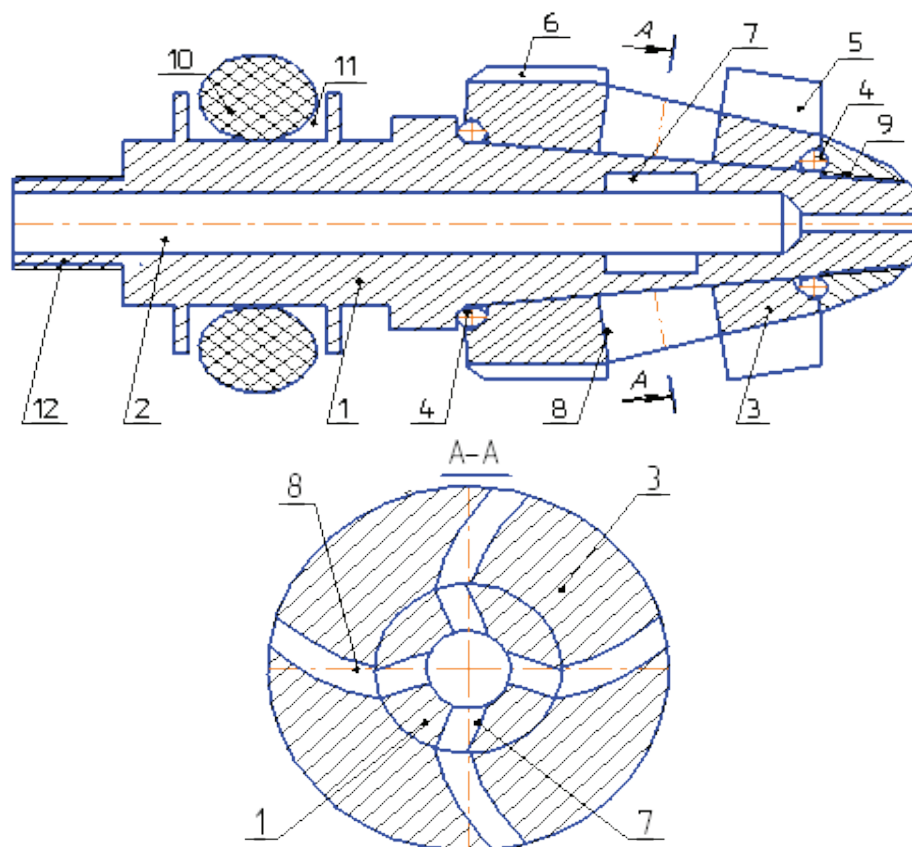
Конструктивная схема устройства для очистки внутренней поверхности трубопроводов
